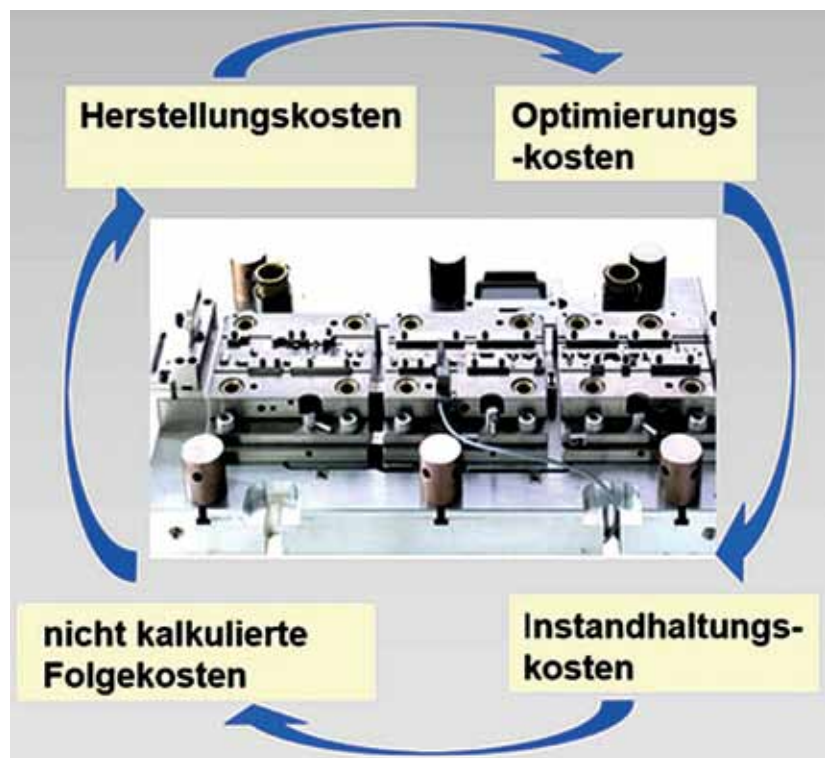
Das WEMA-Werkzeugmanagement ist eine umfassende und lückenlose Softwarelösung, insbesondere für Stanz- und Spritzgießbetriebe. Damit haben Werkzeugbauer ein Tool das die Werkzeugkosten transparent macht und somit die Kosten drastisch senkt
